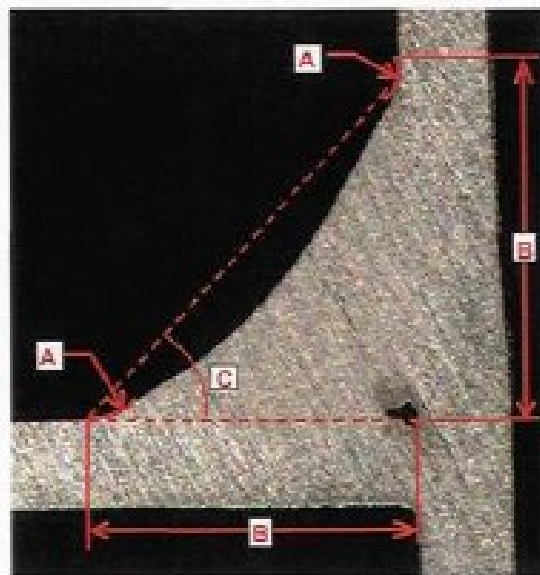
Exemple de coupe d'un cordon de soudure (43)
